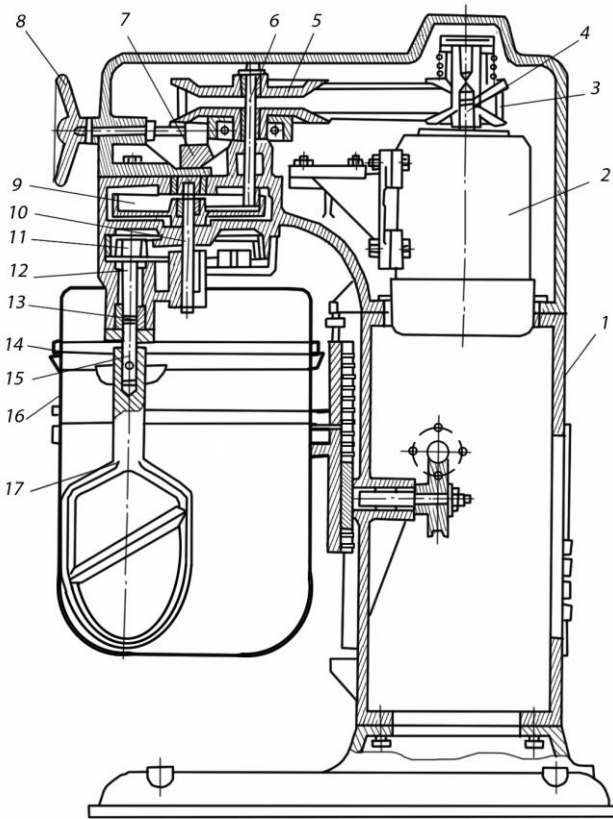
Збивальна машина МВ-35: 1 – станина; 2 – електродвигун; 3 – пас; 4 – нижній диск ведучого шків; 5 – ведений шків; 6 – вал-шестерня; 7 – вилка; 8 – маховик механізму регулювання; 9 – зубчасте колесо; 10 – вал; 11 – нерухоме зубчасте колесо; 12 – планетарний механізм; 13 – корпус планетарного механізму; 14 – обичайка; 15 – вал; 16 – бачок; 17 – збивач
